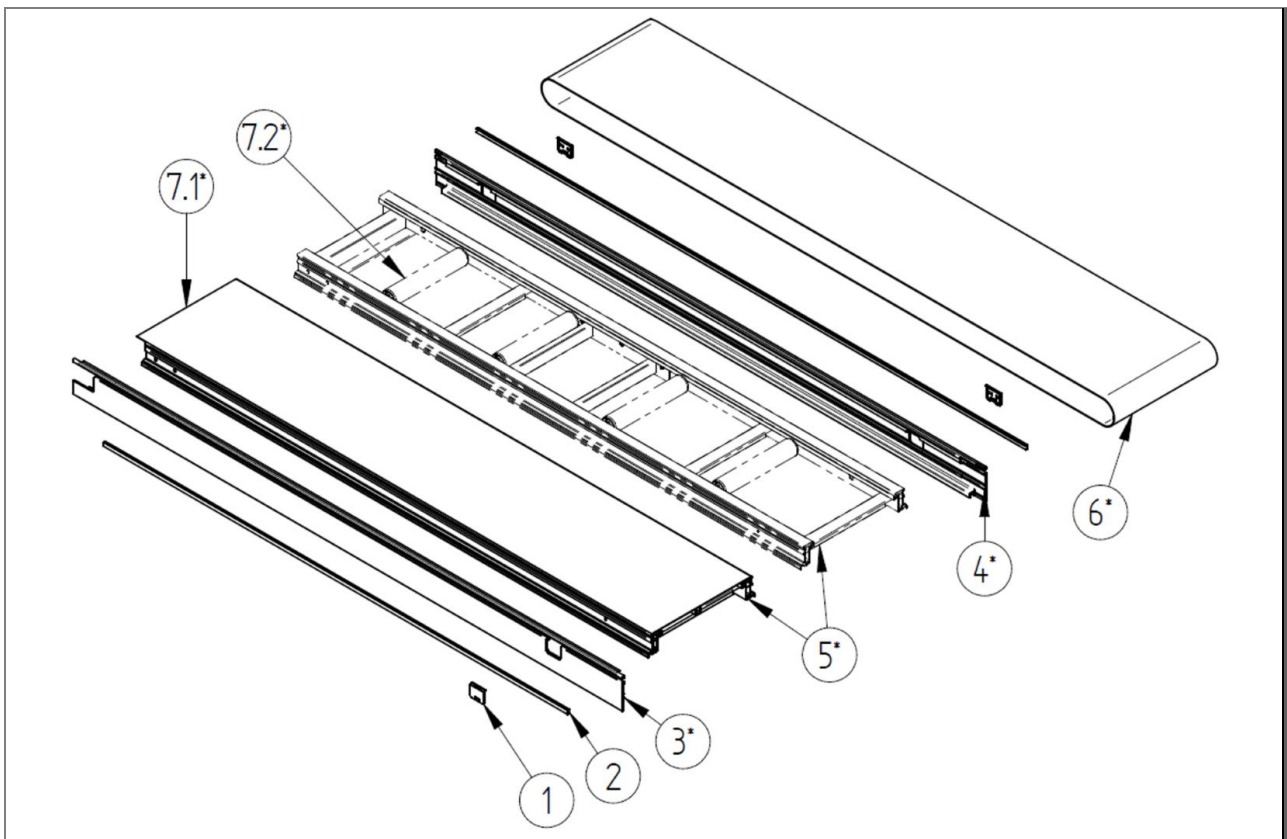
Lista de piezas: del cuerpo de la cinta transportadora GL0 y GL7 - U.116.0002.00
